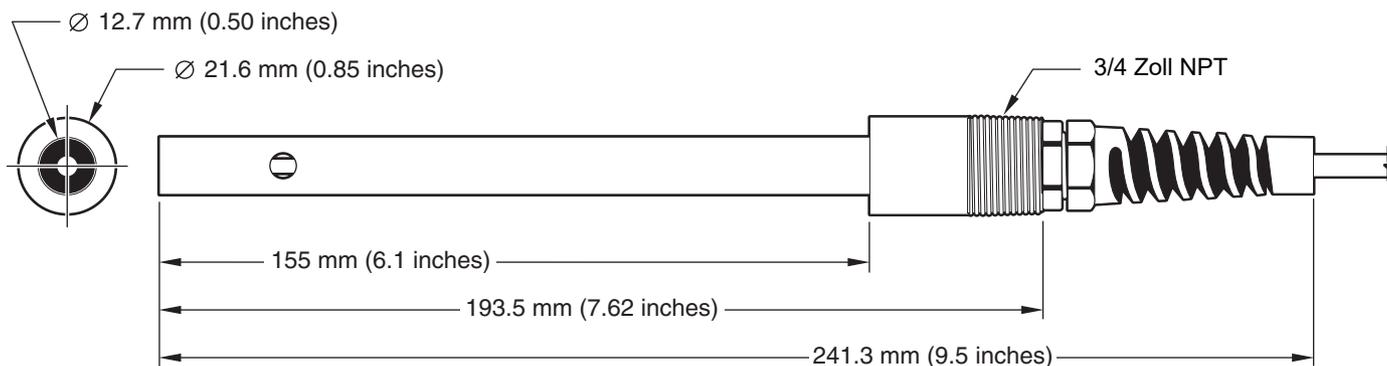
Druckdichter Sensor, 0,75 Zoll Durchmesser
